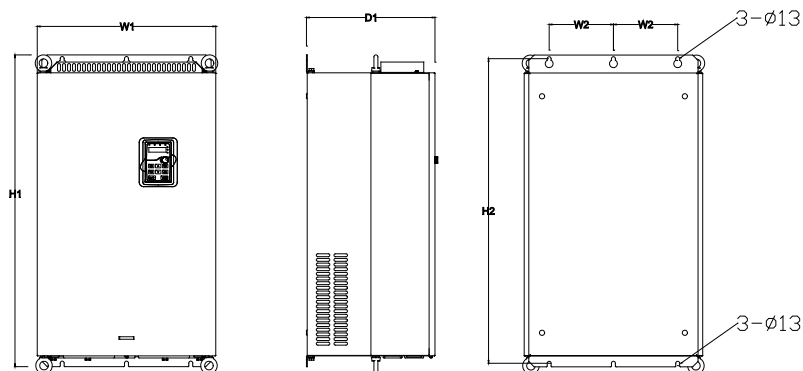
Настенный монтаж 132 – 200 кВт
